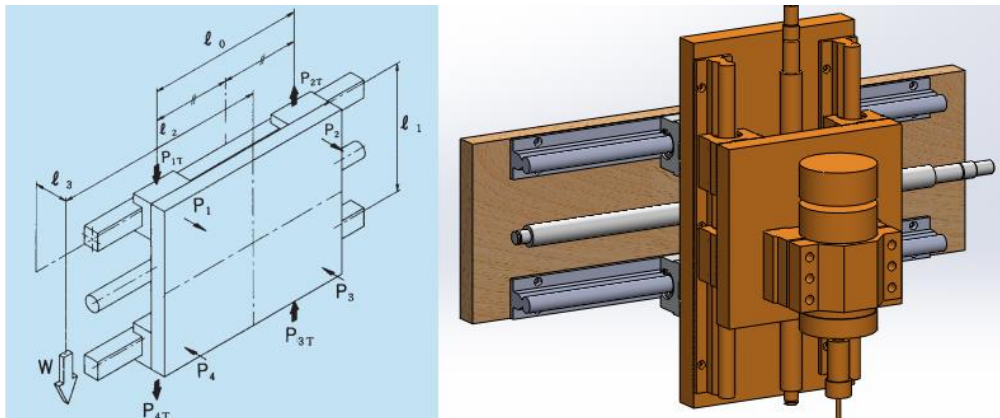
Parámetros que determinan las cargas del eje “X”
